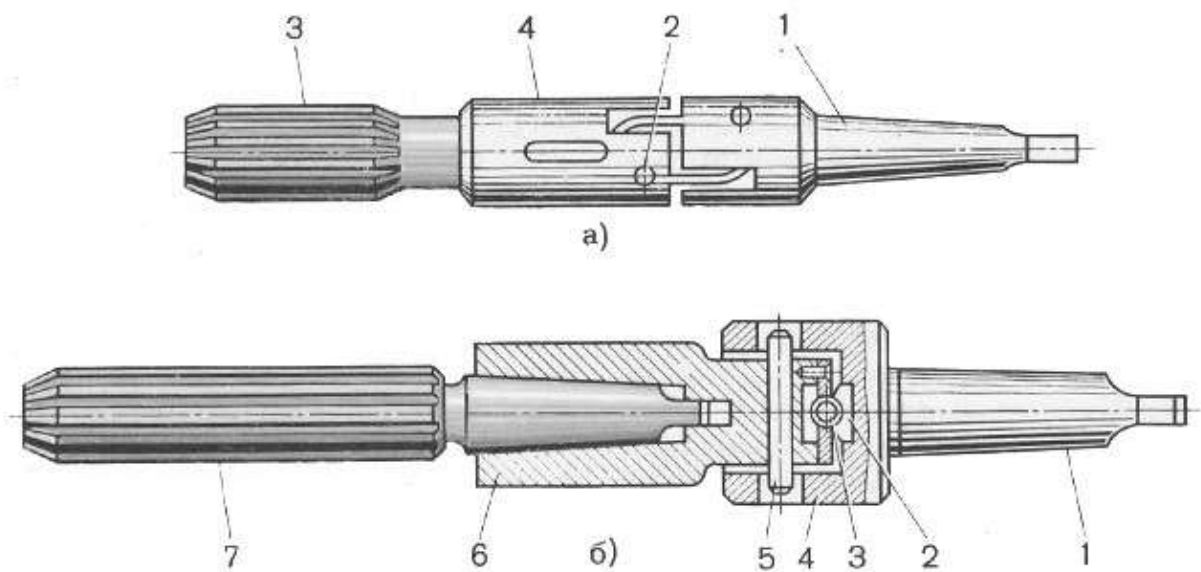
Оправки, що коливаються, для операцій розгортання.
